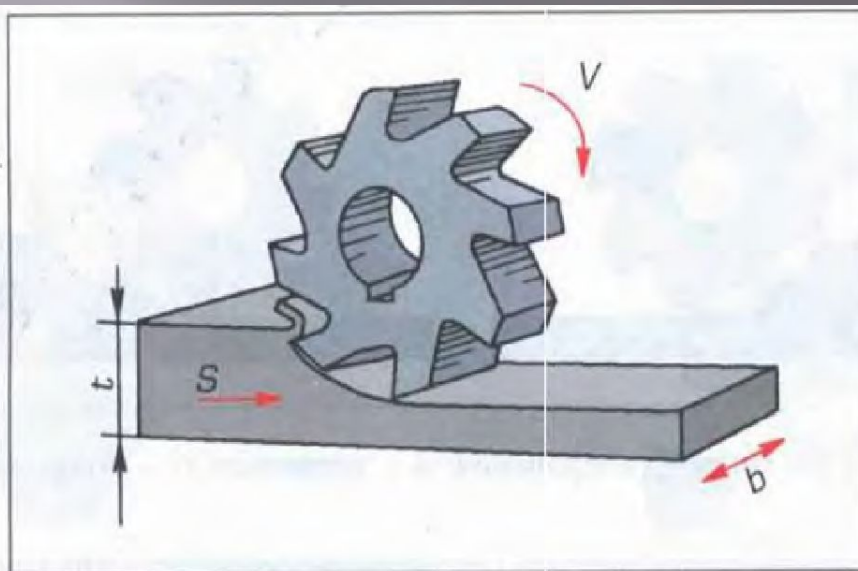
Схема фрезерования: t – глубина фрезерования (толщина снимаемого слоя материала), b – ширина фрезерования, V – скорость резания, S – направление подачи заготовки
